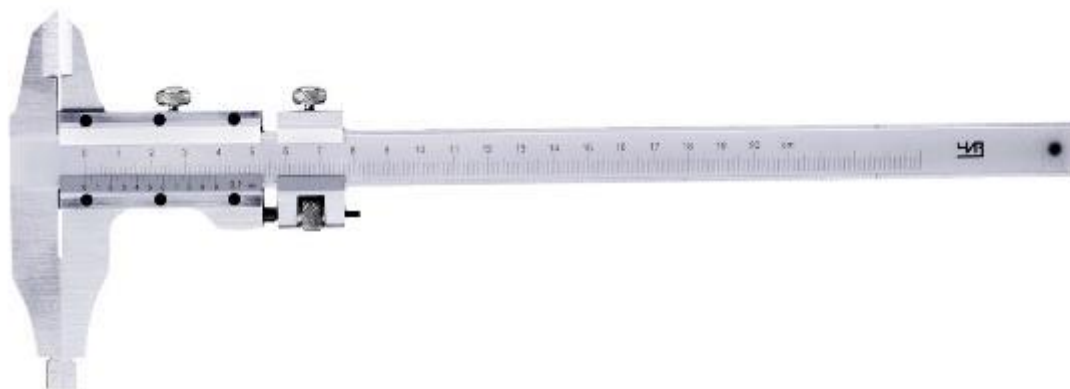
Общий вид штангенциркулей ШЦ-II
